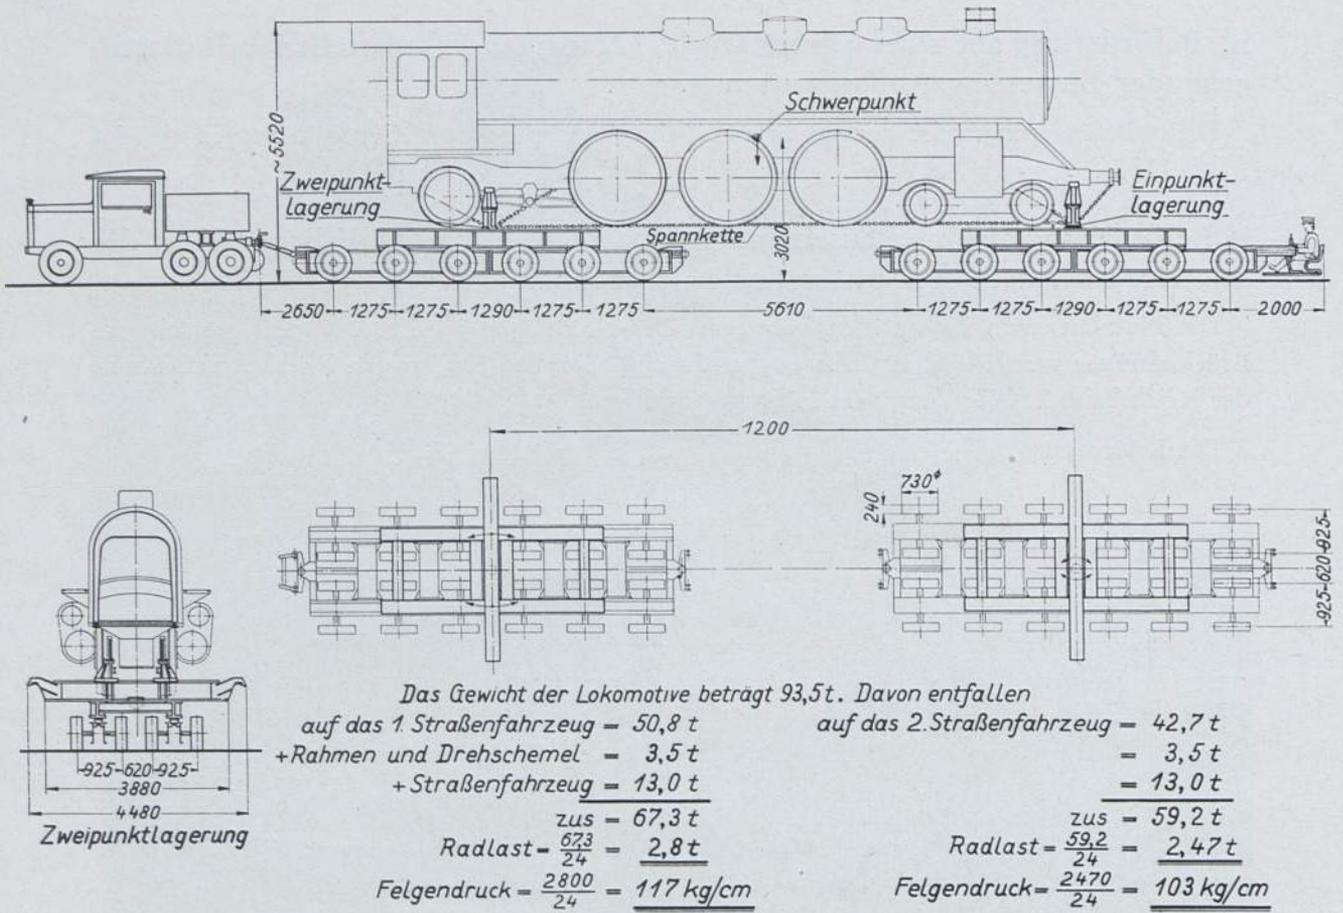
Entwurf für die Beförderung einer 93,5 t schweren Schnellzuglokomotive.
